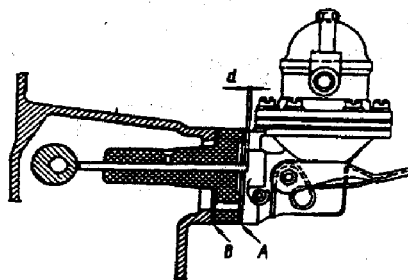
Esquema para instalação da bomba de combustível: A - junta de espessura 0,27 - 0,33 mm; B - junta de espessura 0,70 - 0,80 mm; d - saliência do acionador.
